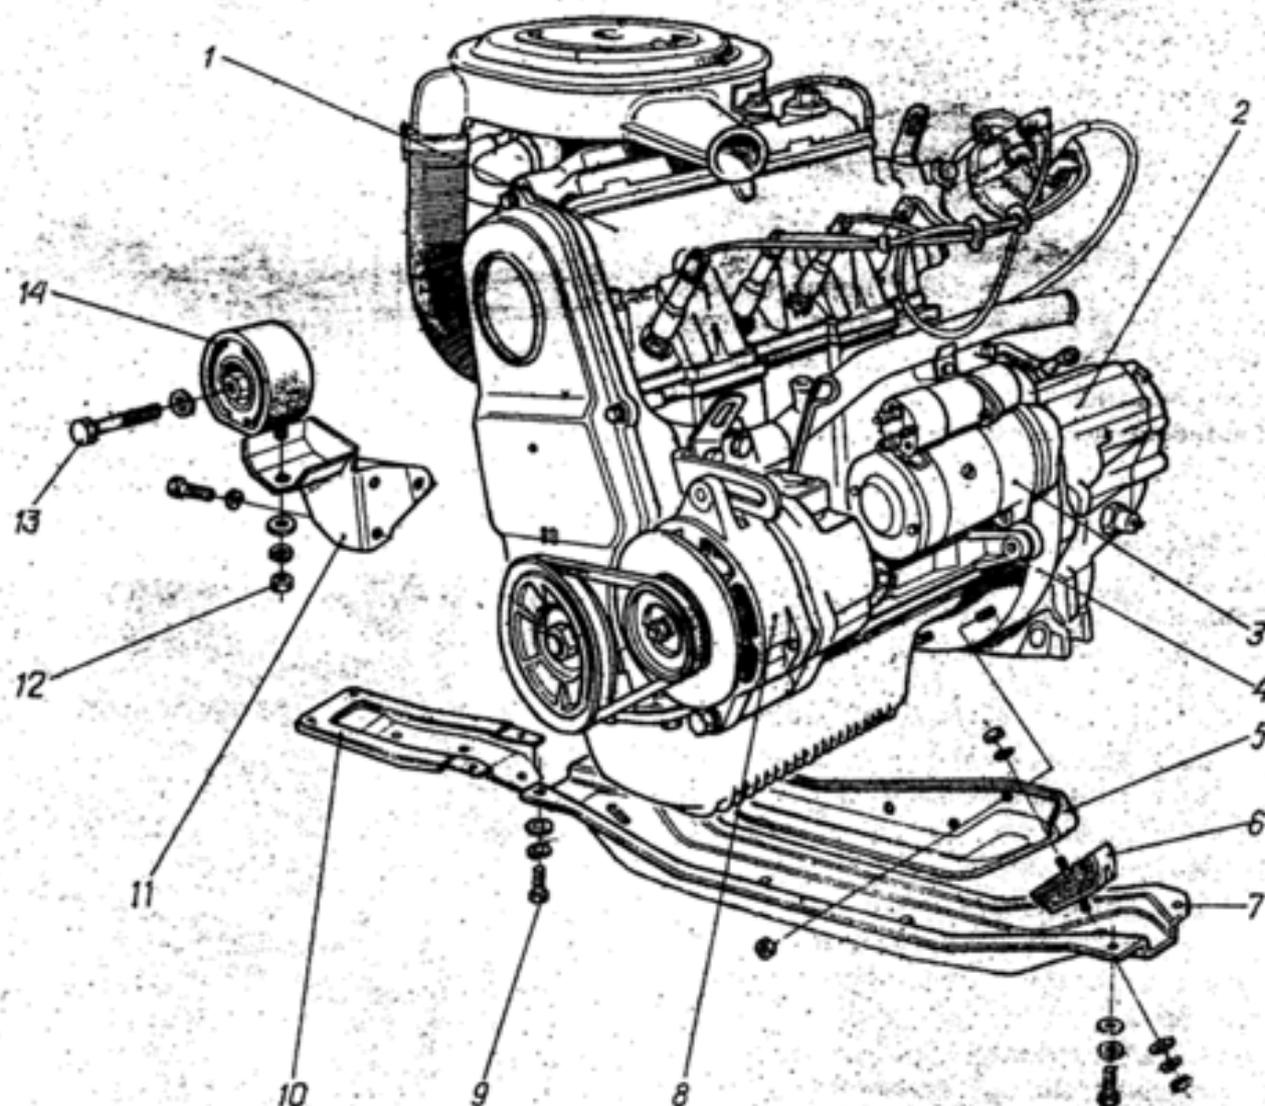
Силовой агрегат и его крепление: 1 - двигатель; 2 - коробка передач; 3 - стартер; 4 - сцепление; 5 - поперечина; 6 - подушка нижняя; 7 - балка; 8 - генератор; 9 - болт крепления балки; 10 - усилитель тоннеля пола; 11 - кронштейн; 12 - гайка крепления подушки к кронштейну; 13 - болт крепления верхней подушки; 14 - подушка верхняя
